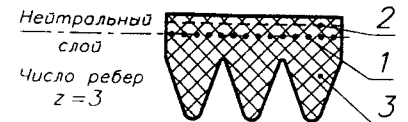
Конструкция поликлиновых ремней: 1 - кордткань; 2 - обкладка; 3 - наполнитель (резина)
